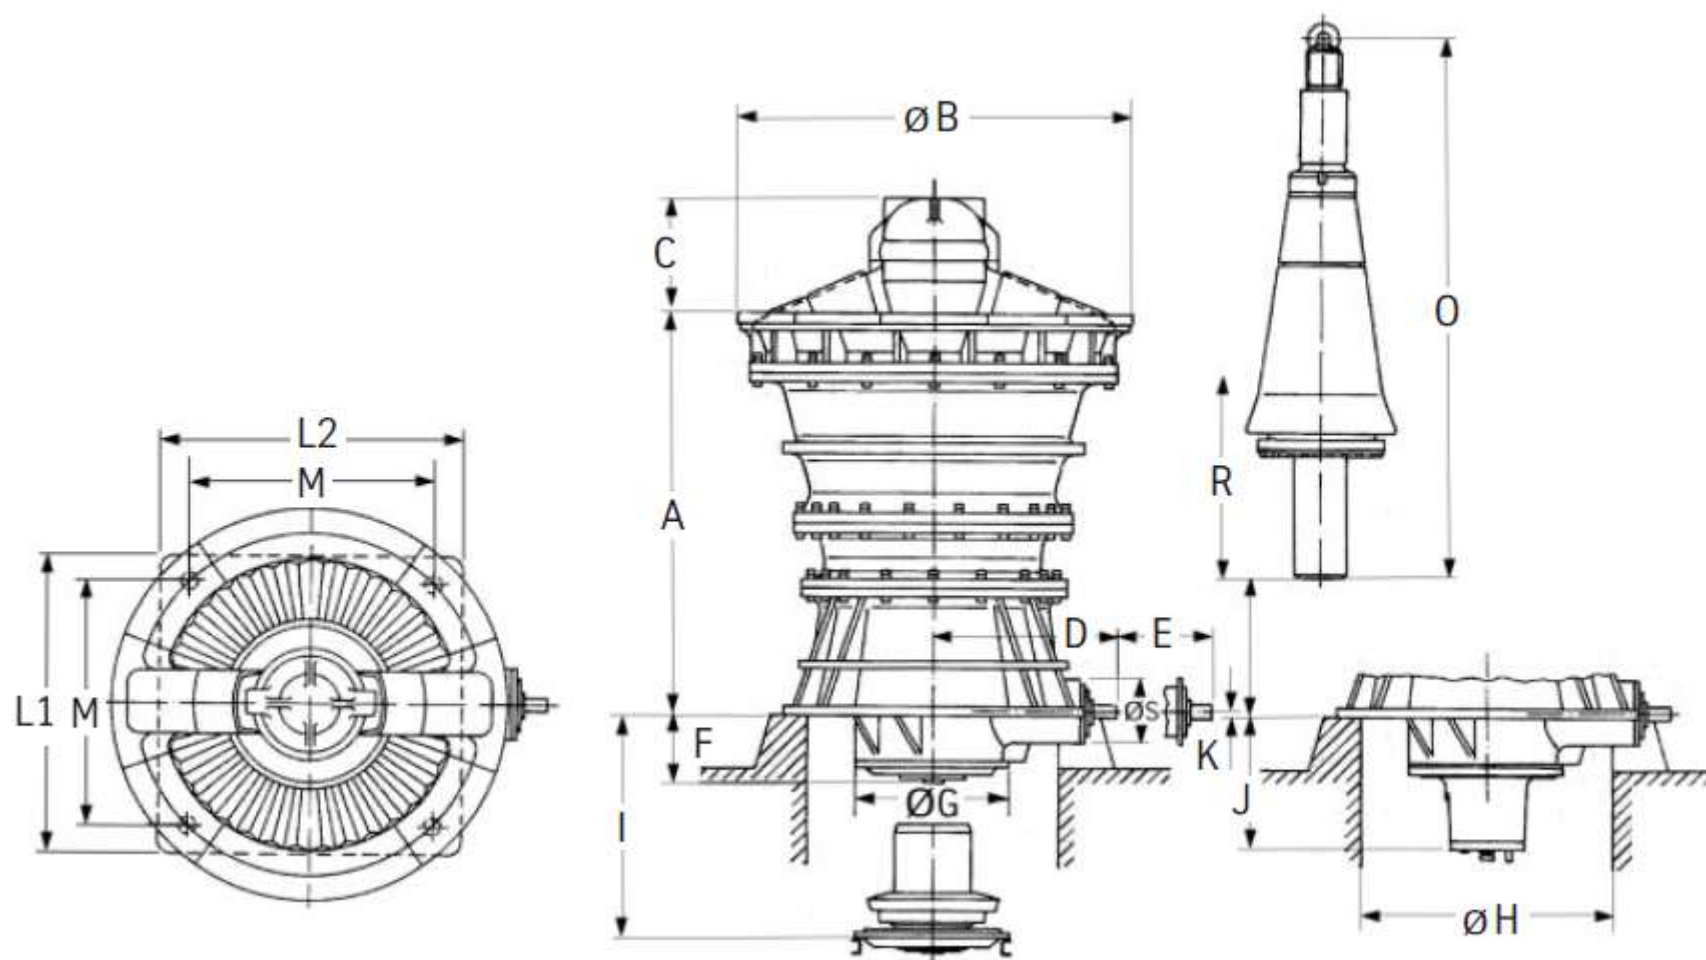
Dimensões de um britador giratório (Thssenkrupp).
